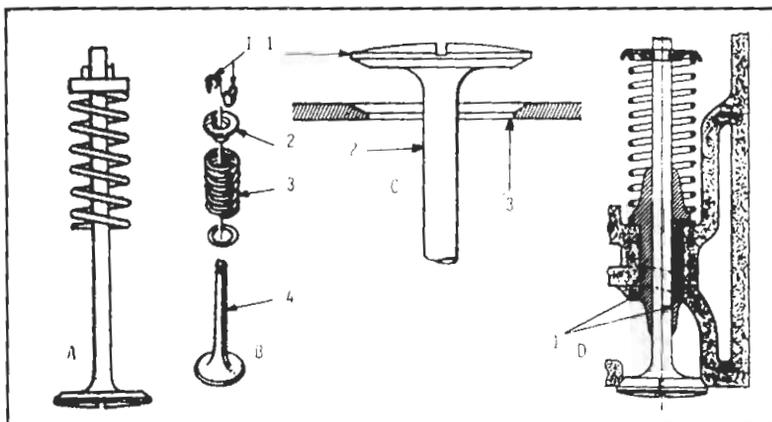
Detalles de las válvulas y su montaje. A) Conjunto de válvula, platillo y muelle montados. B) Despiece: 1.- Chavetas. 2.- Platillo. 3.- Muelle. 4.- Válvula. C) Válvula y su asiento: 1.- Cabeza. 2.- Vástago. 3.- Asiento de la válvula. D) Conjunto montado en la culata: 1.- Guía,
